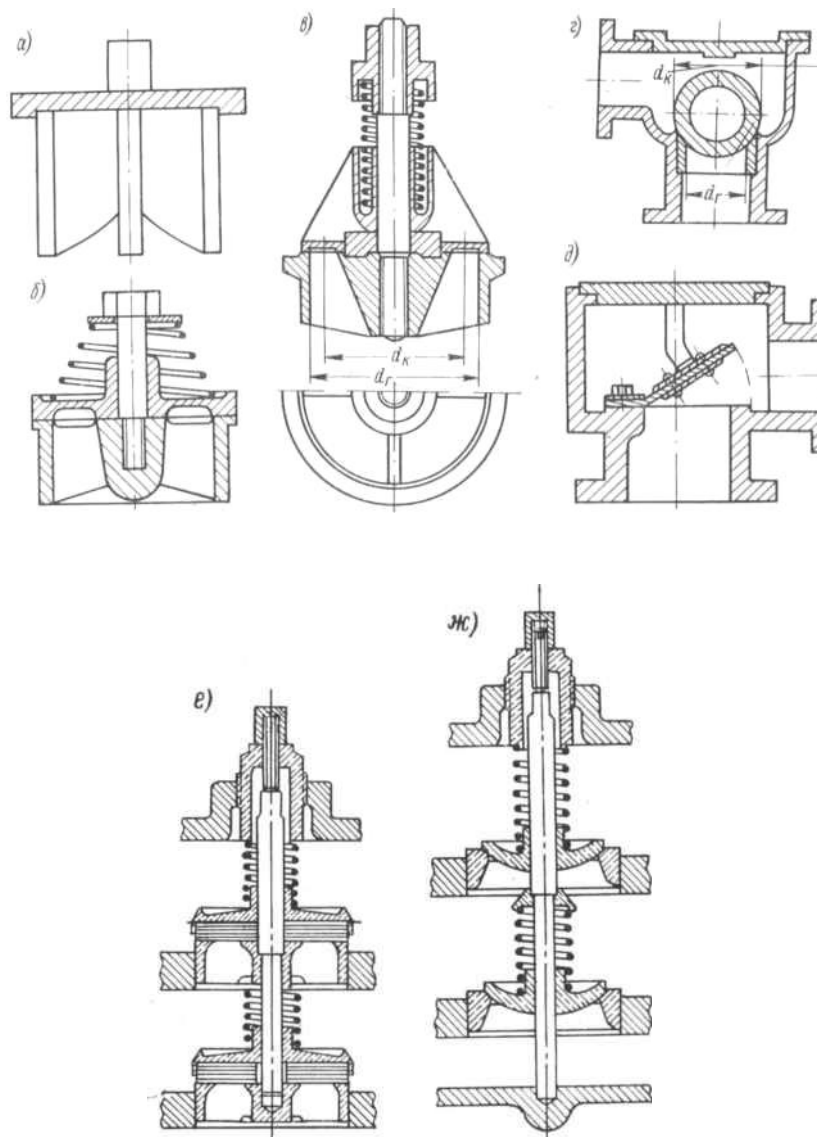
Клапаны поршневых насосов: а — тарельчатый с нижними направляющими ребрами; б — тарельчатый с верхней направляющей; в — однокольцевой; г — шаровой; д — шарнирный; е — пластинчатые; ж — сферический с коническим седлом
